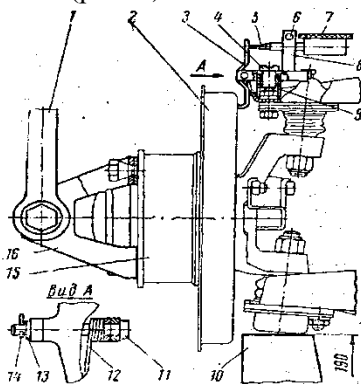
Замер зазора в верхнем шаровом шарнире при помощи приспособления 02.8701.9500 (тормоз условно не показан):
